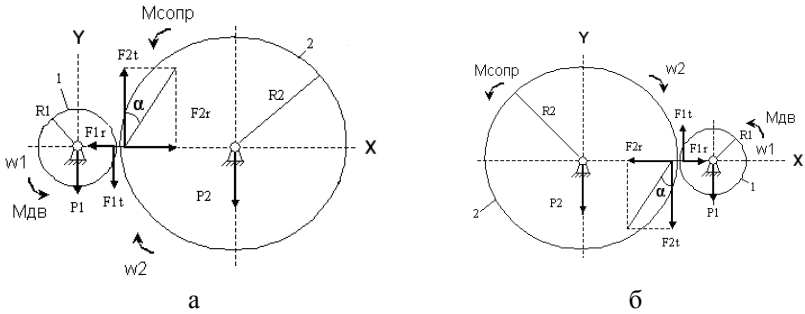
Схема расположения и силового взаимодействия зубчатых колес редукторов клетки 5 (а) и клетки 6(б).
